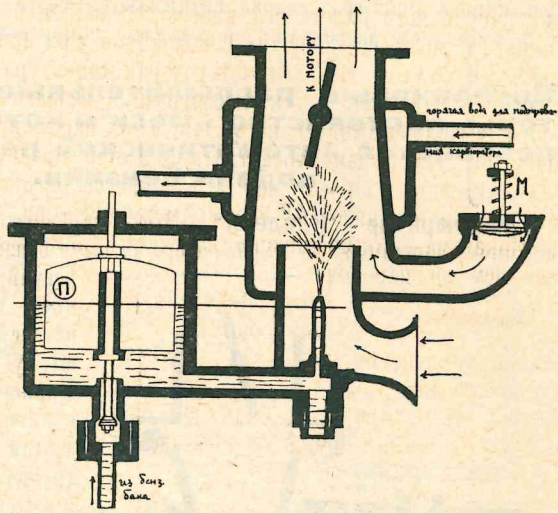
Схема устройства и действия карбюратора с автоматическим впуском воздуха. Как видно из рис., поплавковая камера здесь несколько другого устройства.
